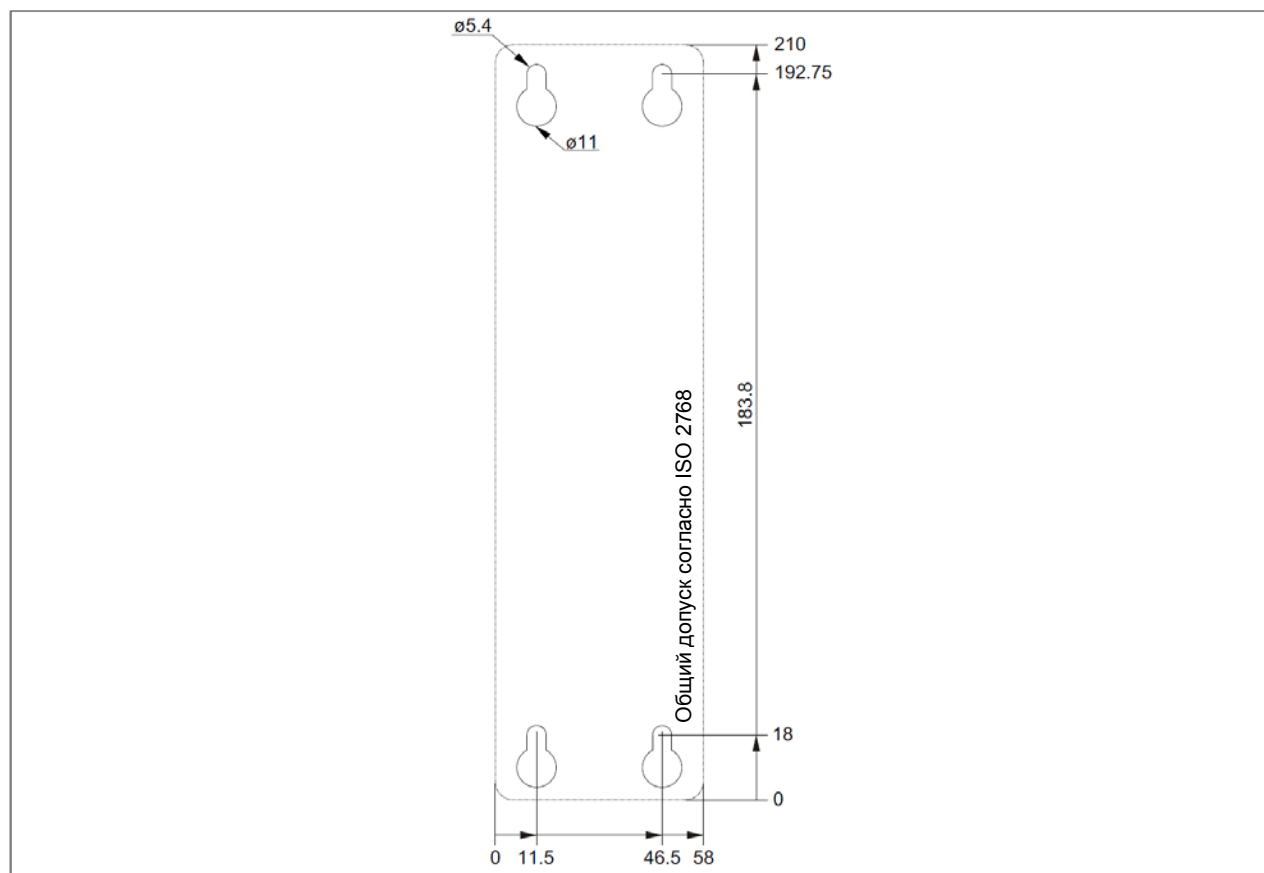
5PC510.SX01-00 - Шаблон для сверления
